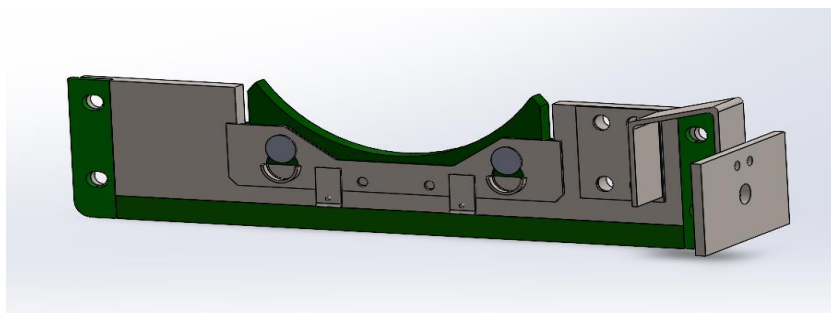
Ensamble de diseño limitador de adhesivo. Fuente: Autor.
